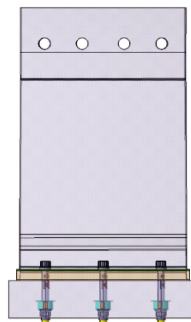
Principe d'assemblage de la bride B2 pour essai.
